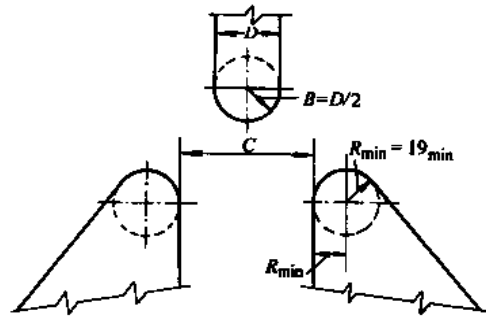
焊接接头弯曲试验弯芯直径和支承架尺寸
